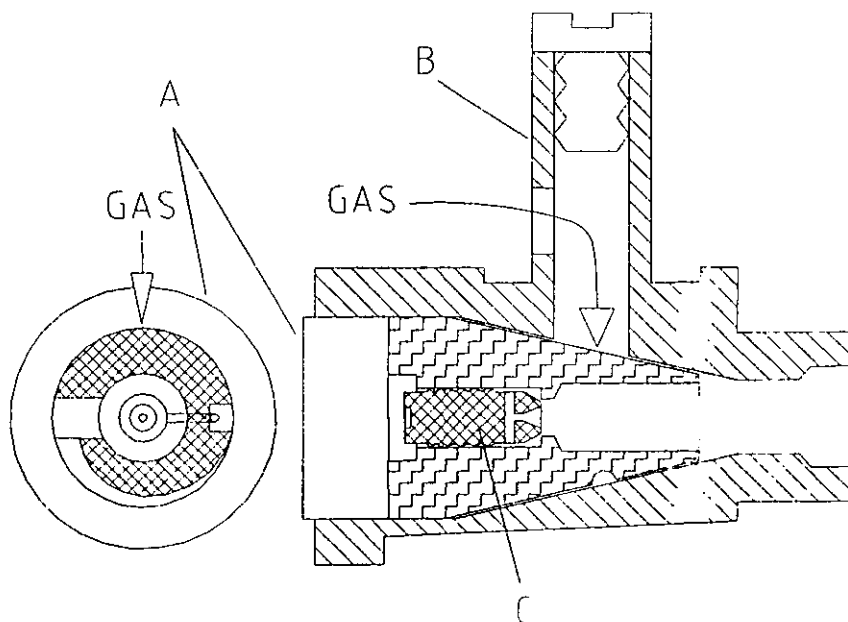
Corte transversal de válvula de macho cónico (cerrada)
